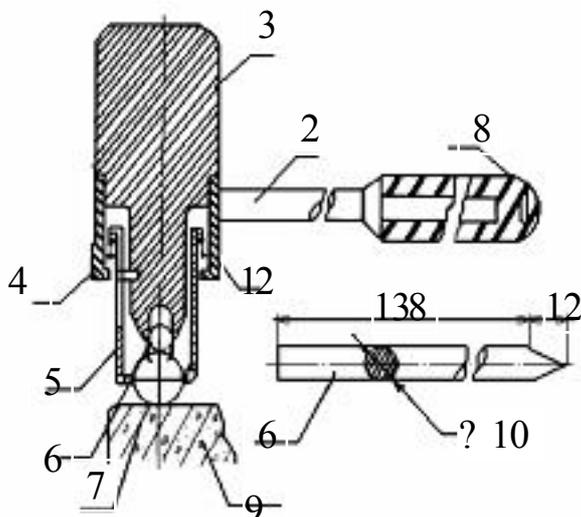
Конструкция эталонного молотка Кашкарова: 1 – корпус; 2 – металлическая ручка; 3 – головка; 4 – пружина; 5 – стакан с отверстиями для шарика и эталонного стержня; 6 – эталонный стержень; 7 – стальной шарик; 8 – резиновая ручка; 9 – испытываемая поверхность
